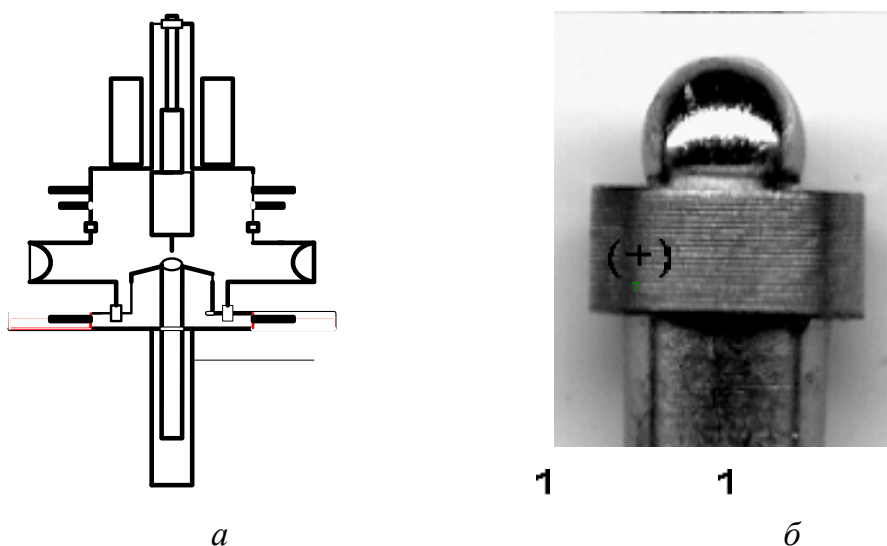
Схема установки сварки в контролируемой атмосфере (а):
